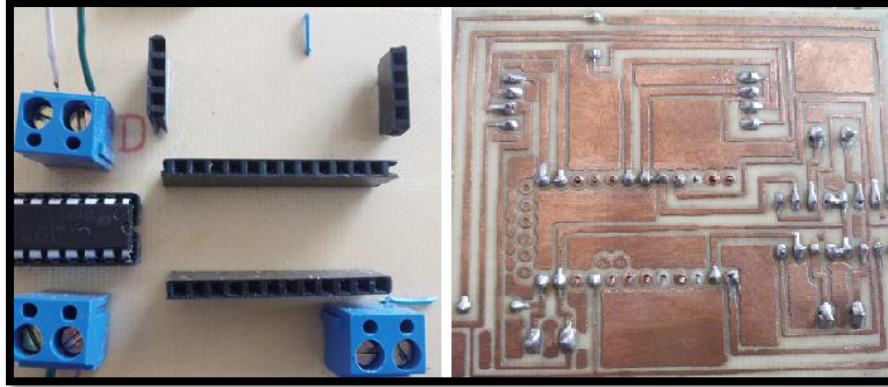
a) Elementos sobre la placa b) Soldadura
